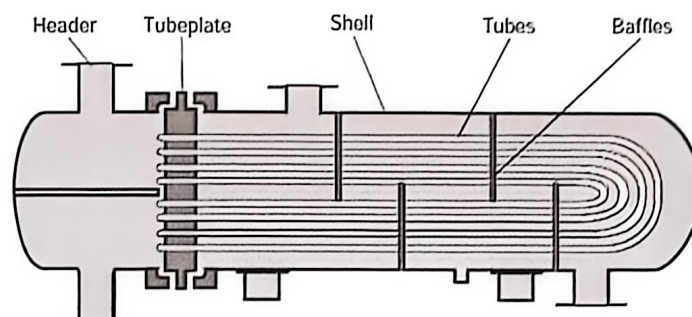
Konstruksi alat penukar kalor jenis Fixed Tube Sheet Heat Exchanger
